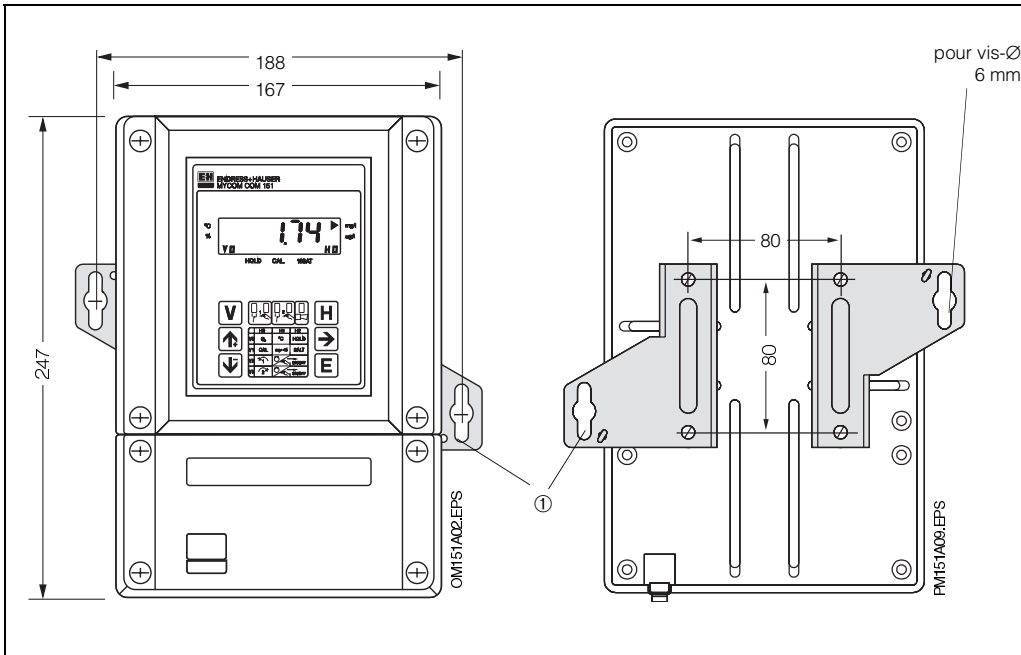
Dimensions du (à gauche) Mycom COM 151
